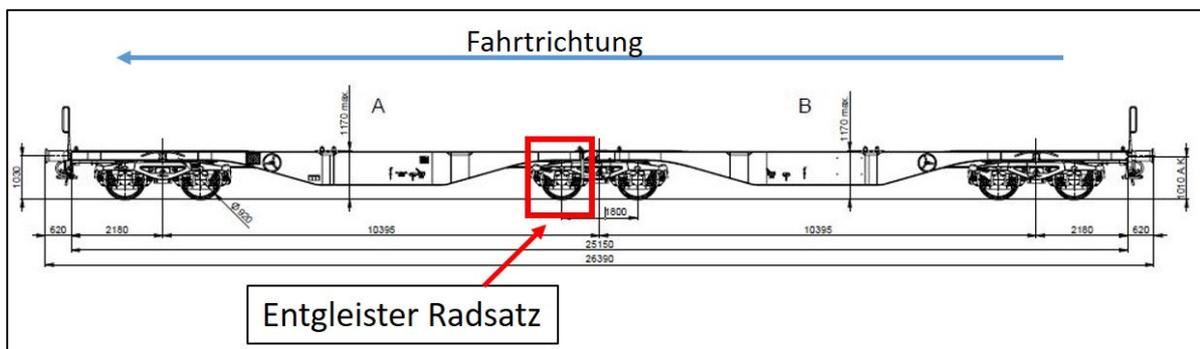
Technische Zeichnung Fahrzeuggattung Sggrss⁶
